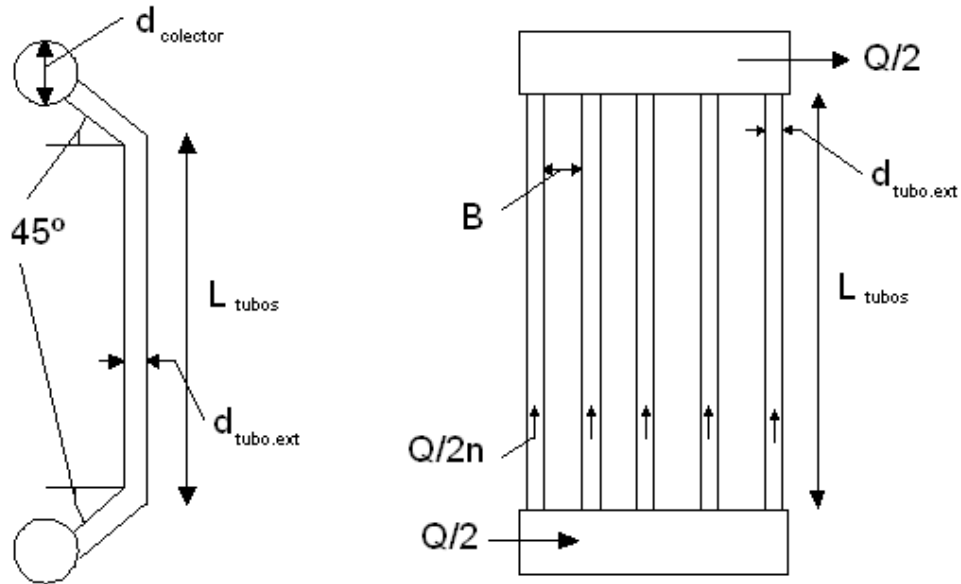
Esquema de un panel del receptor de torre. Izquierda: Vista lateral. Derecha: Vista frontal
